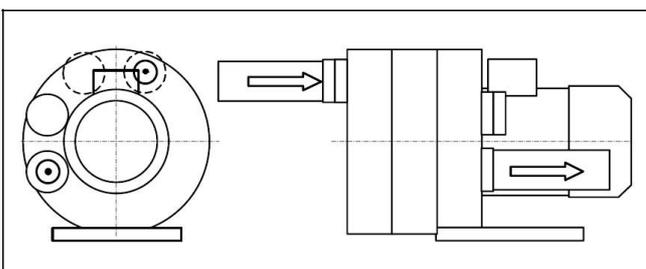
Трехступенчатые вакуумные насосы/компрессоры с тремя рабочими колесами
